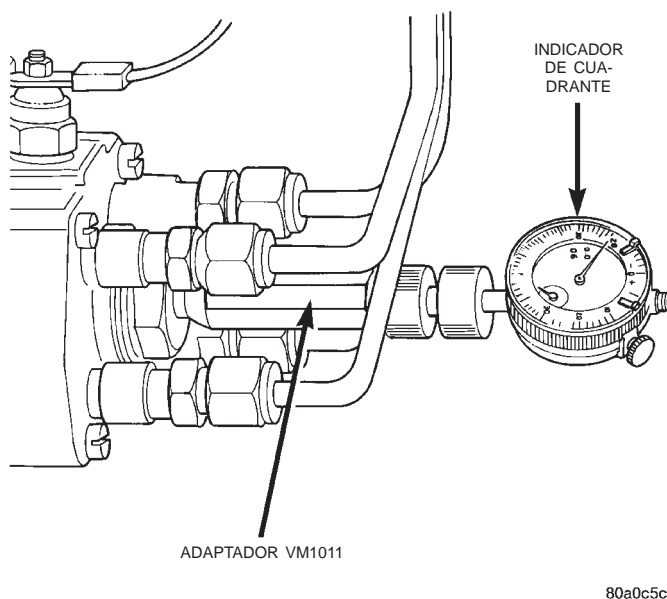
Instalación de la herramienta especial de indicador de cuadrante y adaptador
